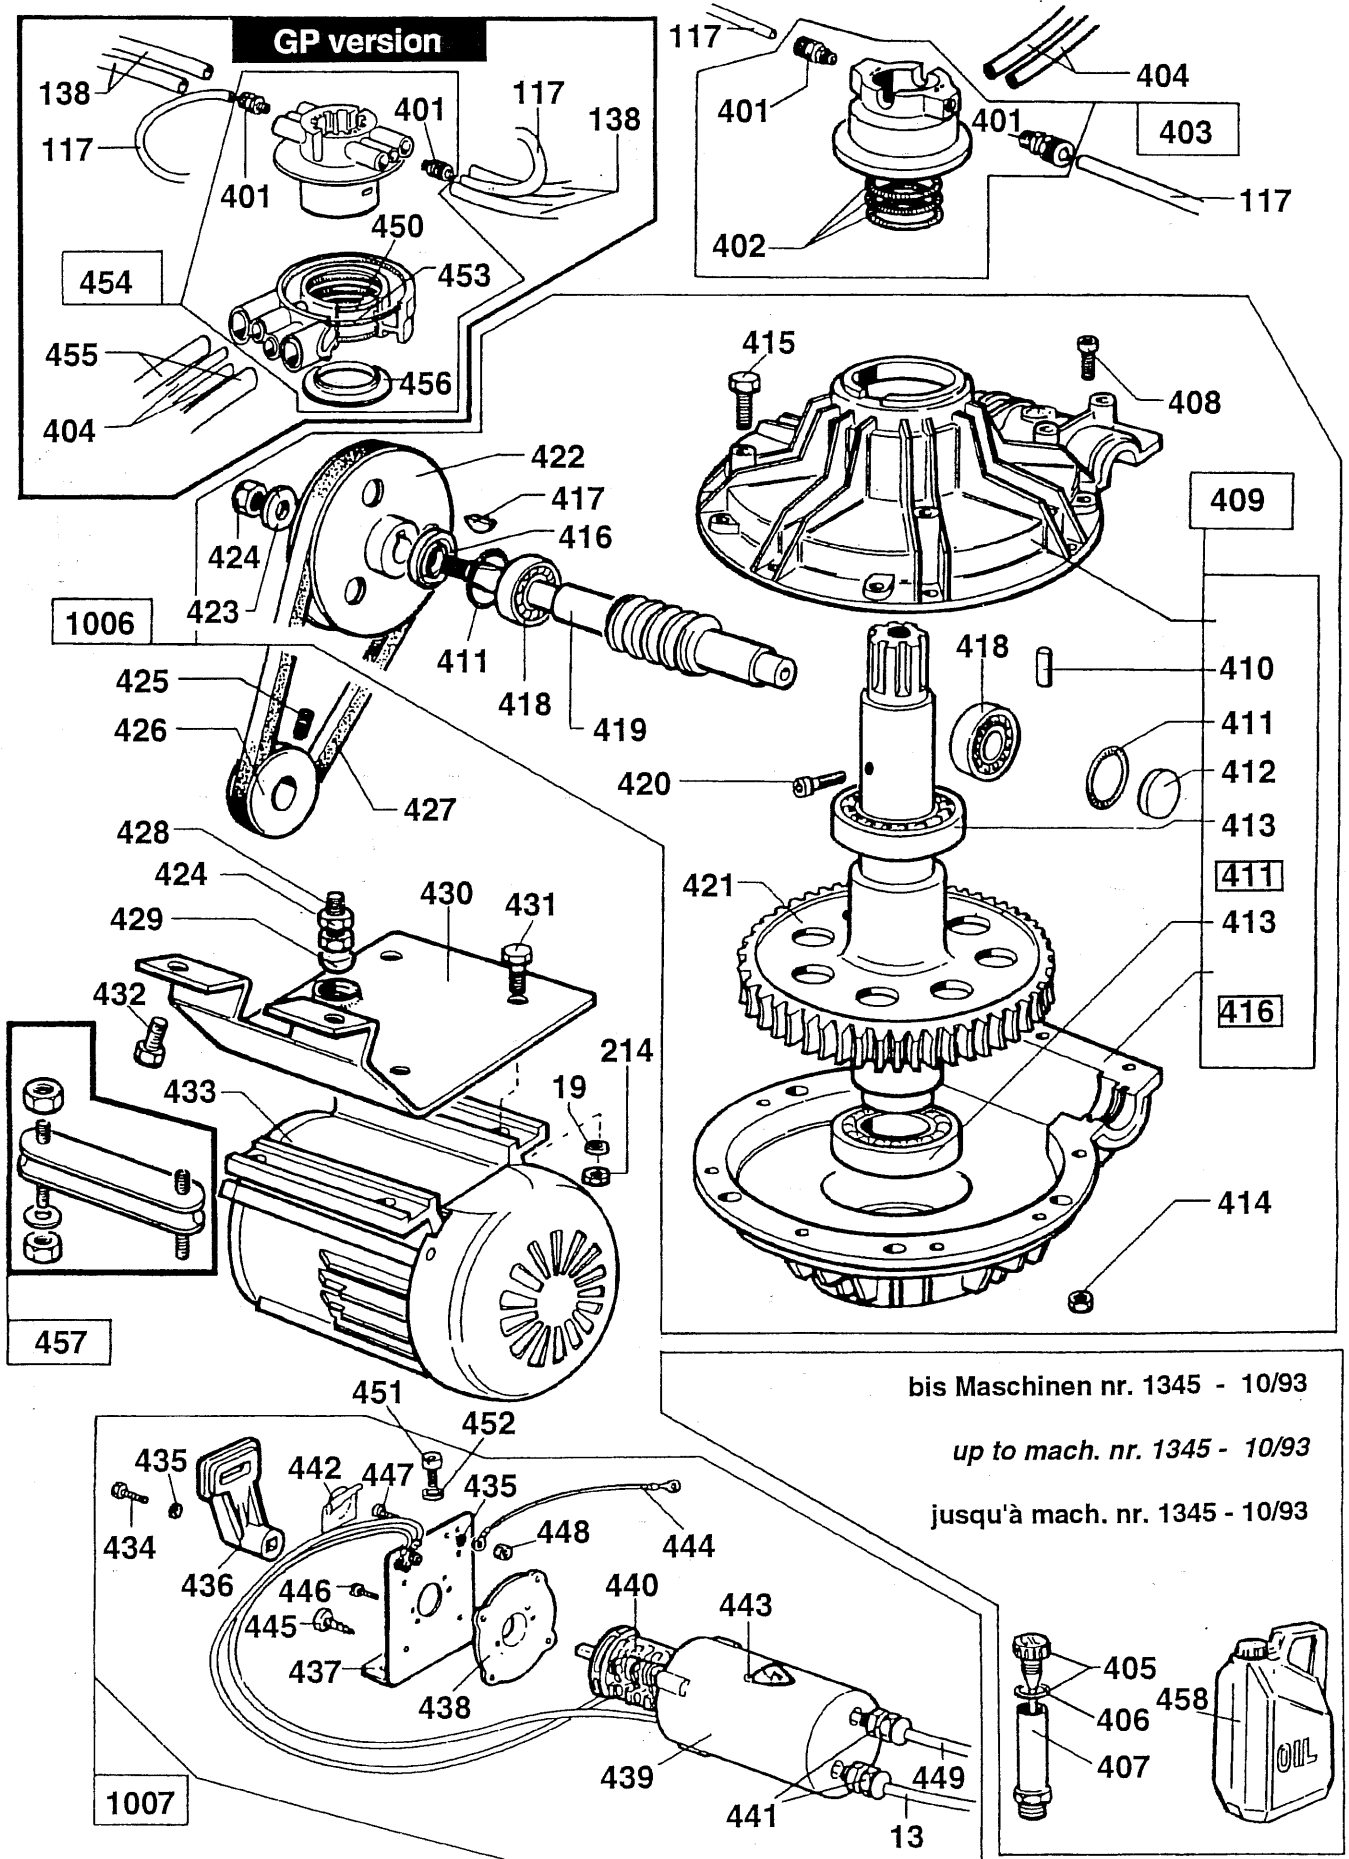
ANTRIEB - DRIVE UNIT - ENSEMBLE D'ENTRAINEMENT
